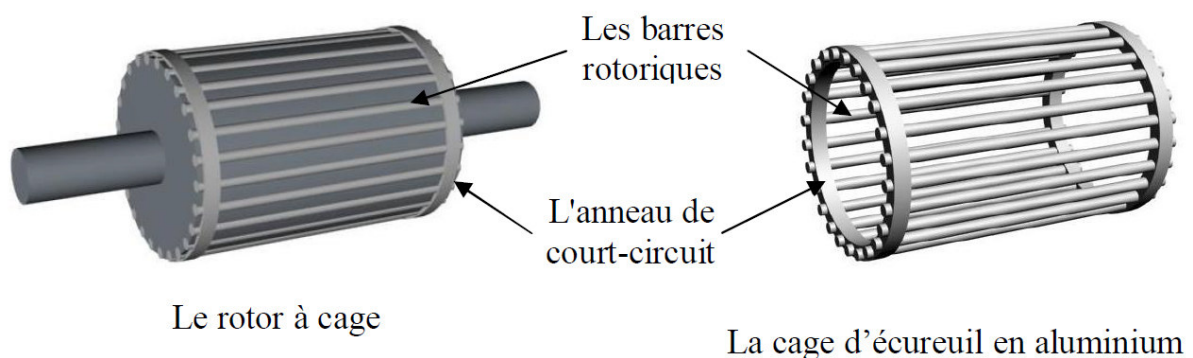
Photo du rotor d'une machine asynchrone. [3]
